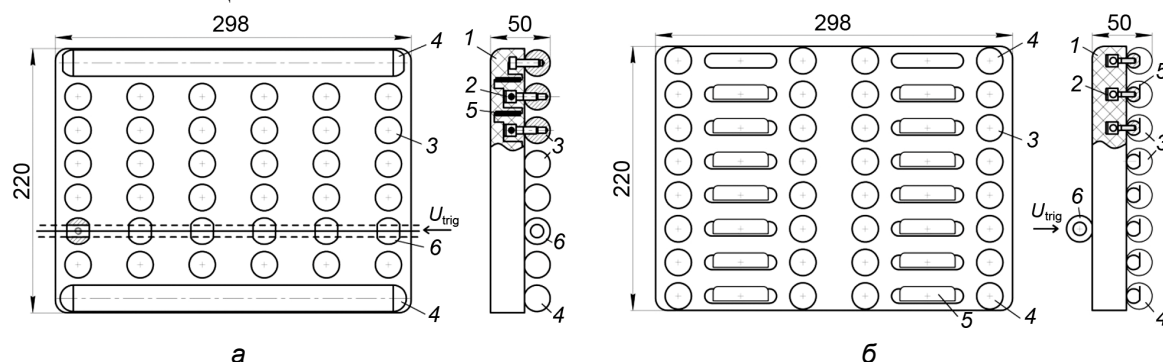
Конструкции двух вариантов разрядника: 1 – корпус разрядника; 2 – детали для крепления электродов; 3 – электроды разрядника; 4 – высоковольтный и низковольтный концевые электроды; 5 – резистивный делитель напряжения или коронирующие острия; 6 – пусковые электроды
